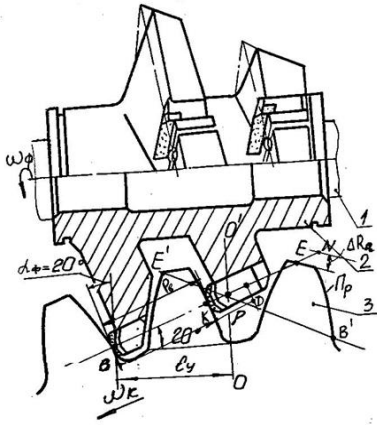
Схема станочного зачеплення правого корпусу фрези та оброблюваного колеса
